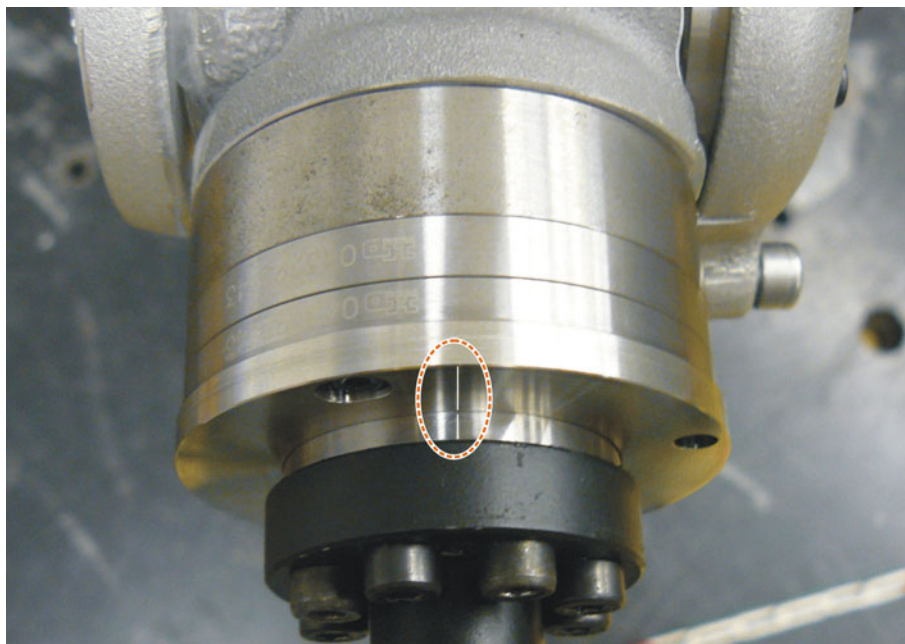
Position de calibration d'A6 - vue d'en haut
